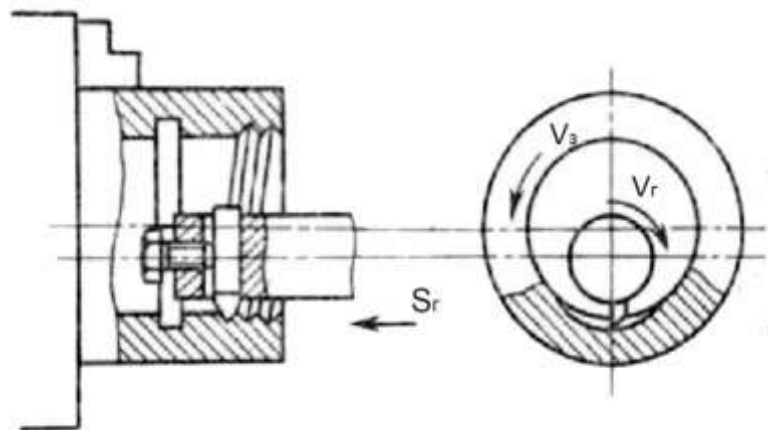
Схема обробки внутрішнього різьблення вихровим способом.
